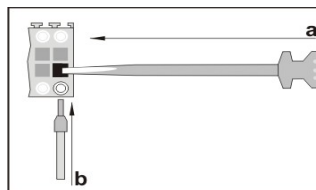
a) inserire il cacciavite; b) inserire il cavo nel morsetto;
